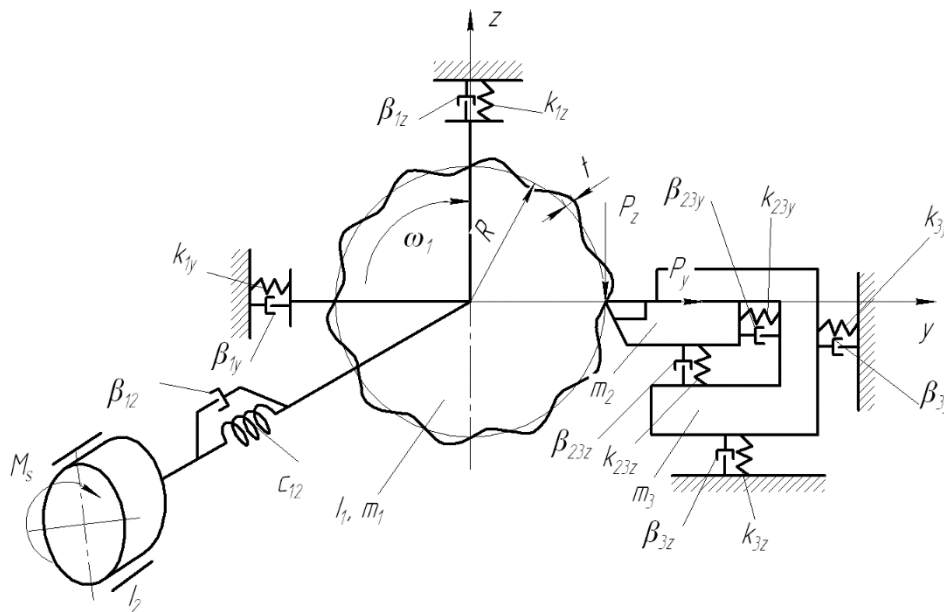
Розрахункова схема еквівалентної багатомасової системи для дослідження динаміки процесу токарної обробки поверхні із змінною глибиною різання
